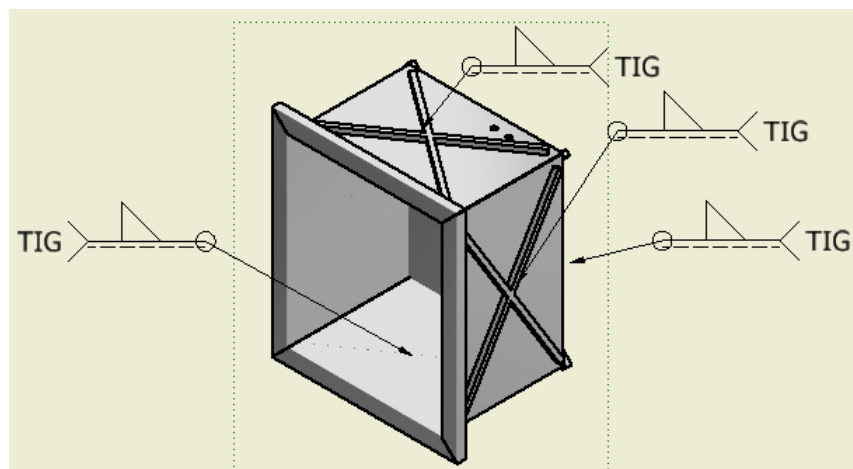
Proceso de soldado para la cámara de trabajo
